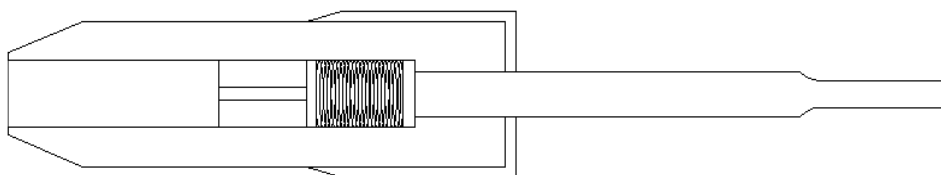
Corte longitudinal da máquina que facilita a introdução da armadura
